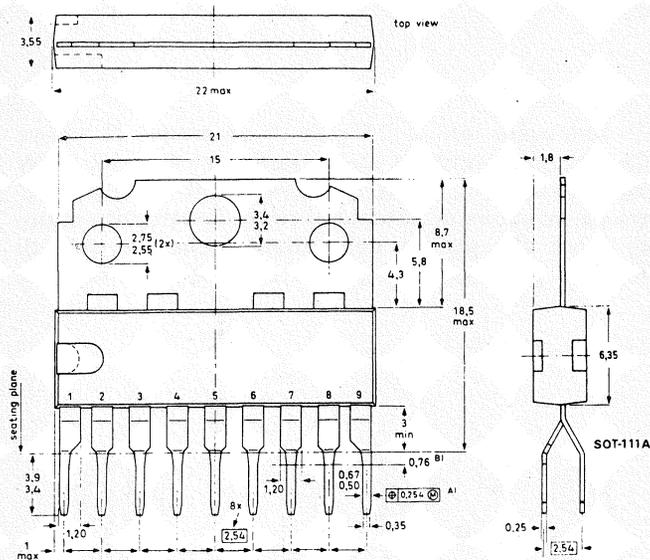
Dimensioni d'ingombro in mm del contenitore SOT-111A.
